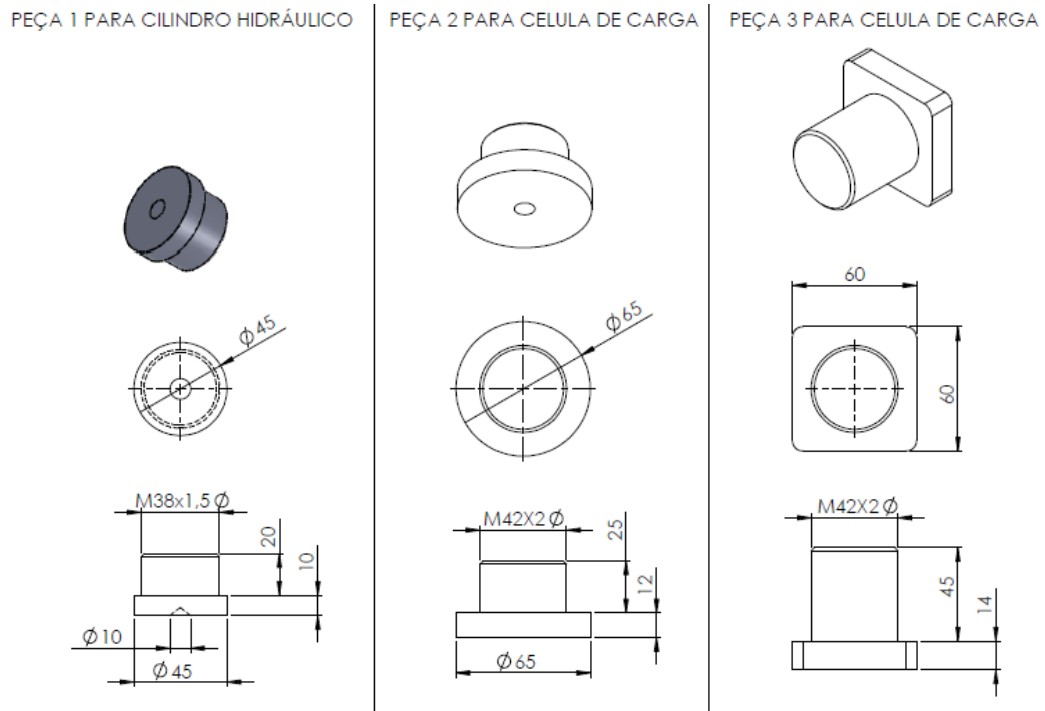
Conjunto de elementos de fixação projetados para o dispositivo de ensaio
